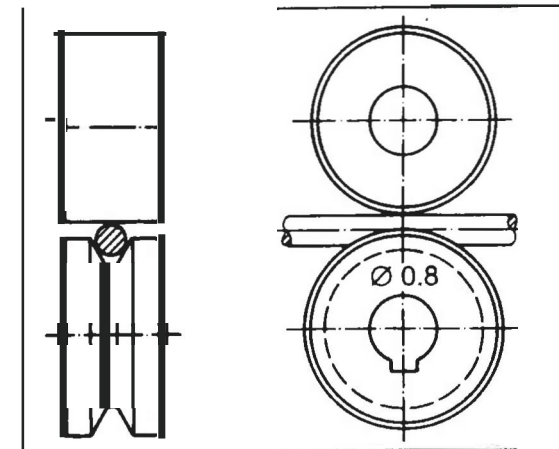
RODILLOS PARA EL SOLDEO MIG/MAG
